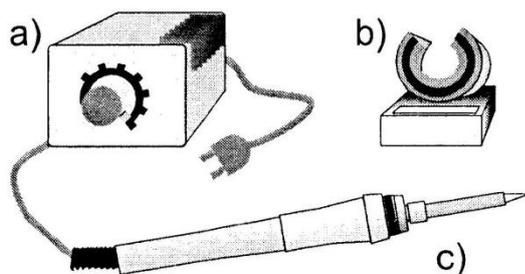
Pájecí techniky měkkého pájení používané v elektrotechnice (zdroj: [14])
